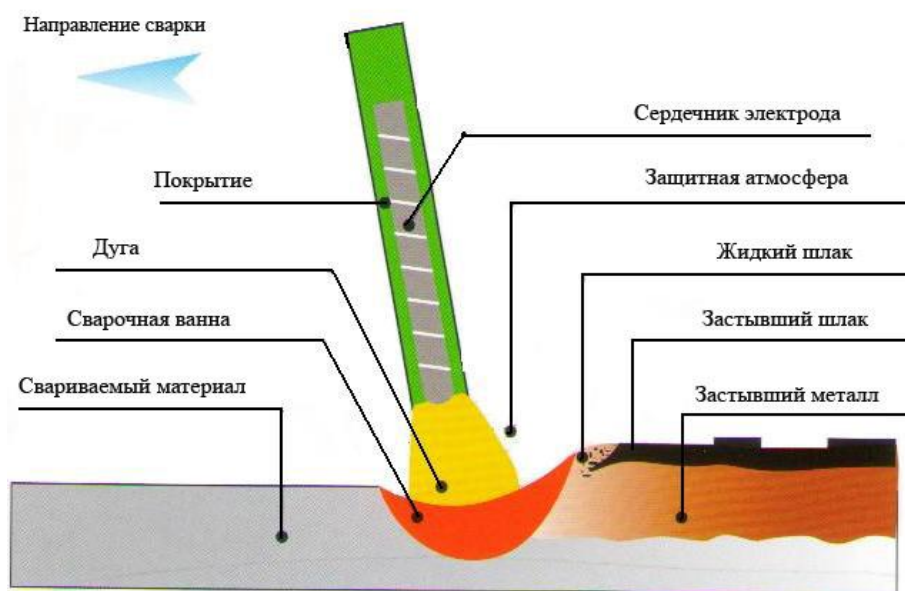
Схема процесса ручной дуговой сварки штучными электродами
